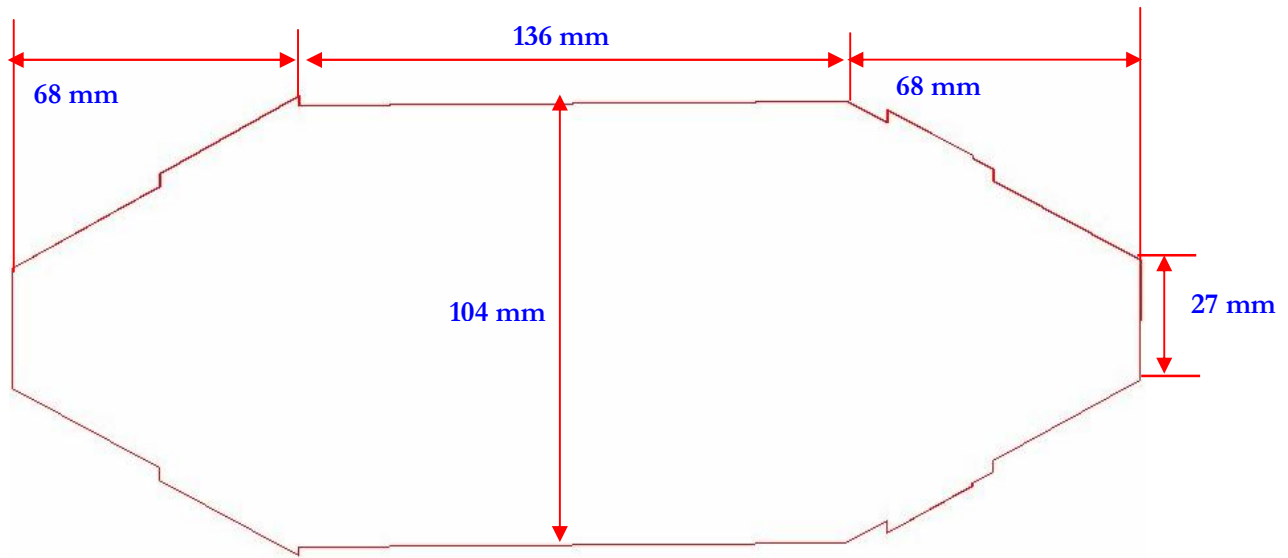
Dimensions et forme du septum de la première cellule réalisée
